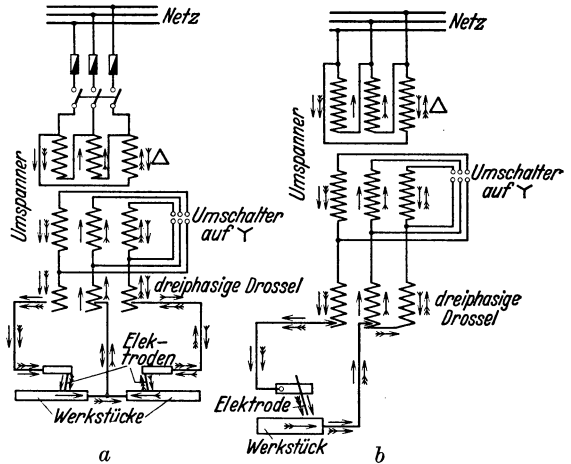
Schaltung einer Drehstromschweißanlage.
